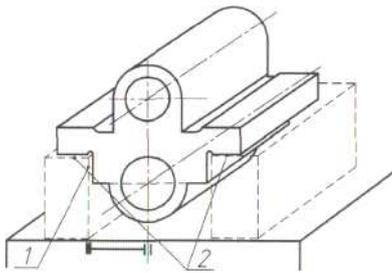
Схема установки заготовки с разделенными базовыми опорными поверхностями: 1 – базовая боковая опорная поверхность; 2 – базовые установочные опорные поверхности
